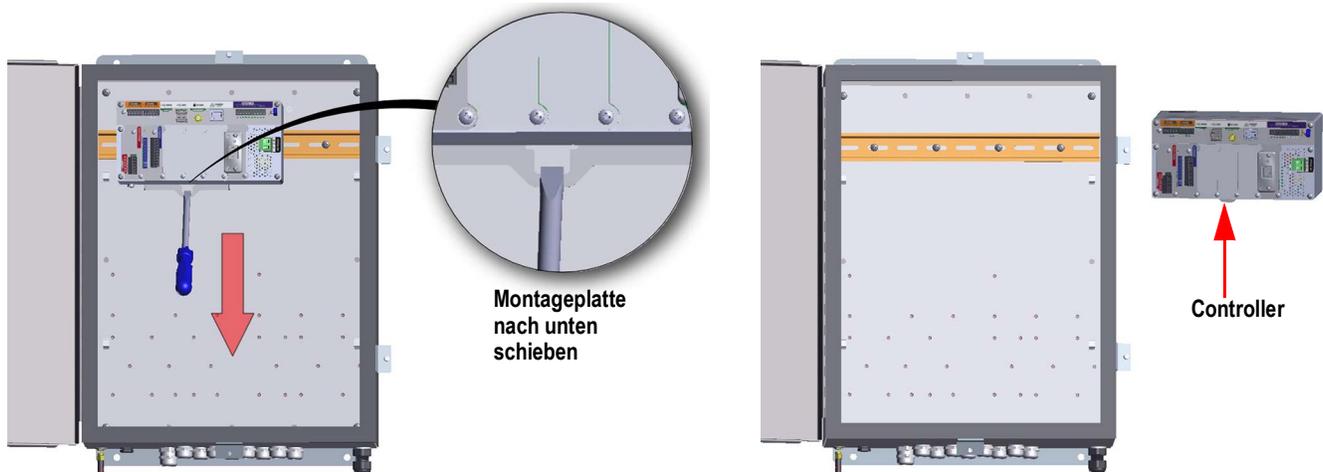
Entfernen des Controllers - Wandmontage
